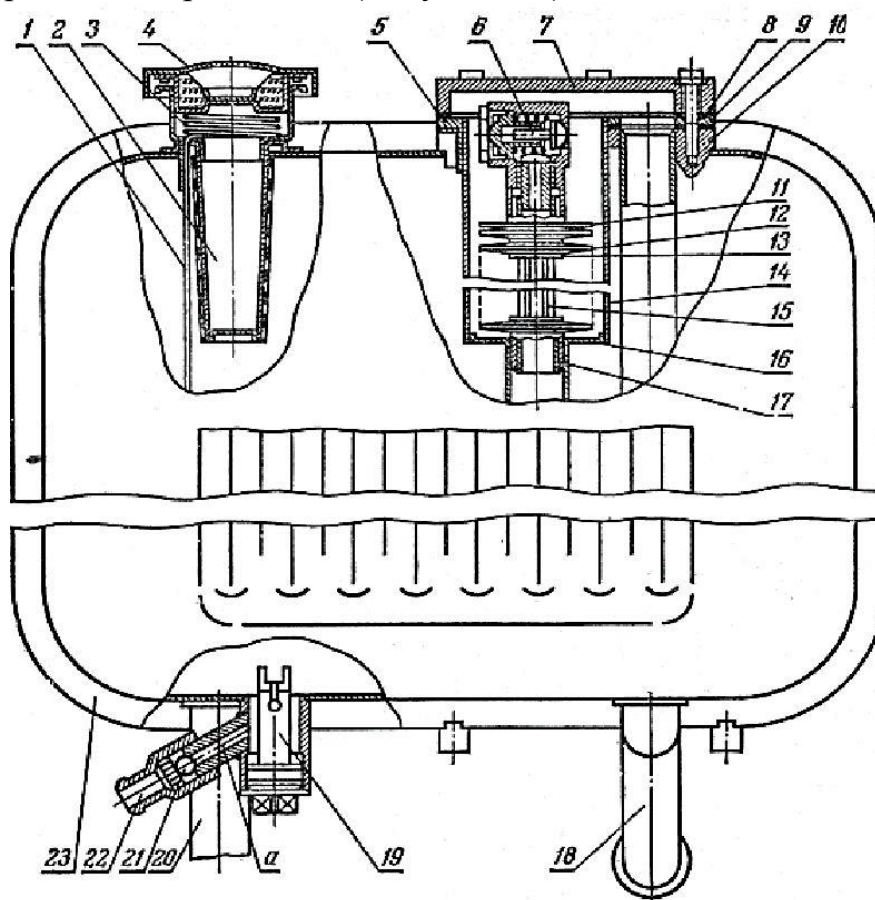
Бак гидросистемы: *a* - сливной канал; 1 - масломерная линейка; 2 - фильтр заливной горловины; 3 - пружина; 4 - крышка заливной горловины; 5, 10 - фланцы; 6 - предохранительный клапан фильтра; 7 - крышка; 8, 9 - прокладки; 11, 13 - шайбы; 12 - фильтрующий элемент; 14 - корпус фильтра; 15 - центральная трубка; 16 - дно корпуса фильтра; 17 - втулка; 18 - сливная труба; 19 - сливная пробка с магнитом; 20 - заборная труба; 21 - запорный шарик; 22 - штуцер; 23 - корпус гидробака
